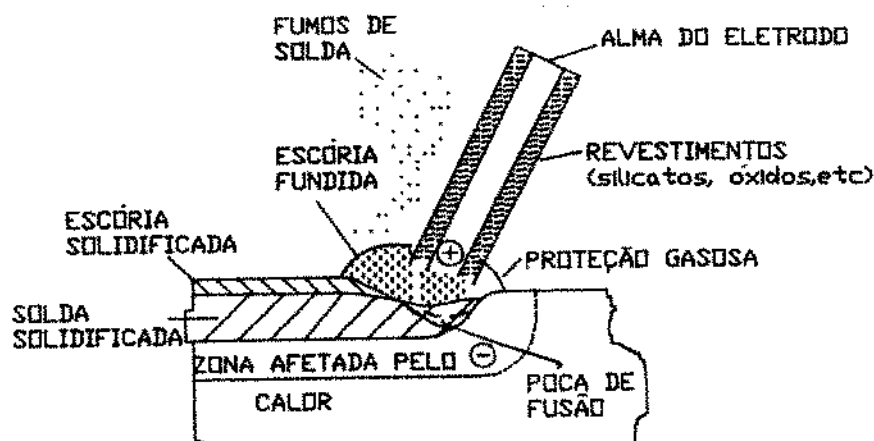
Soldagem a Arco com Eletrodo Revestido [7]
